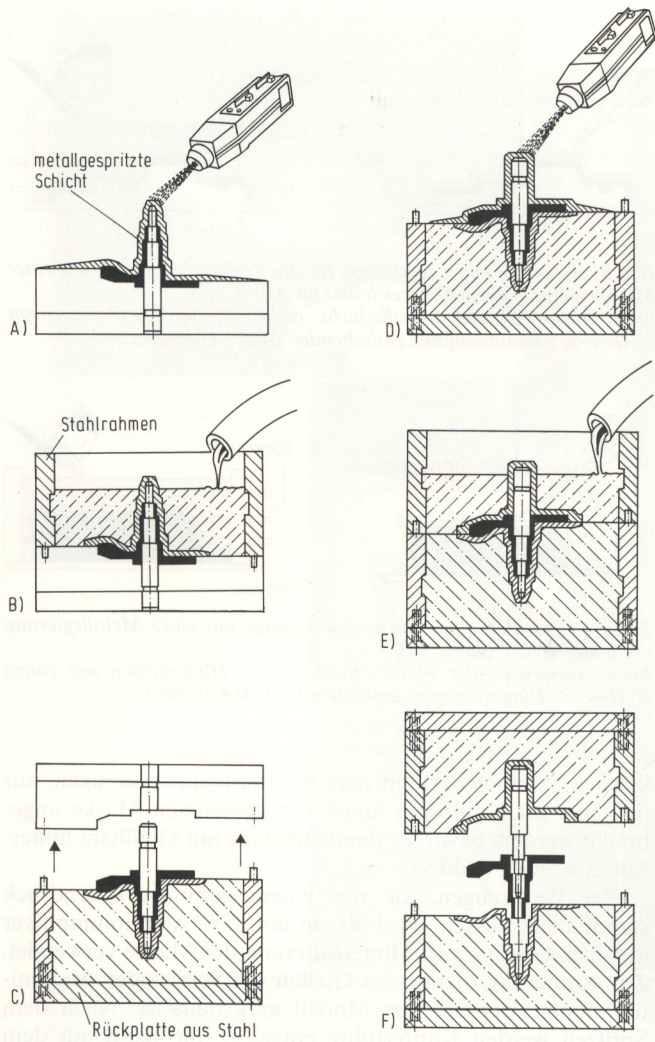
Herstellen eines Spritzgießwerkzeugs mittels Metallspritzen
